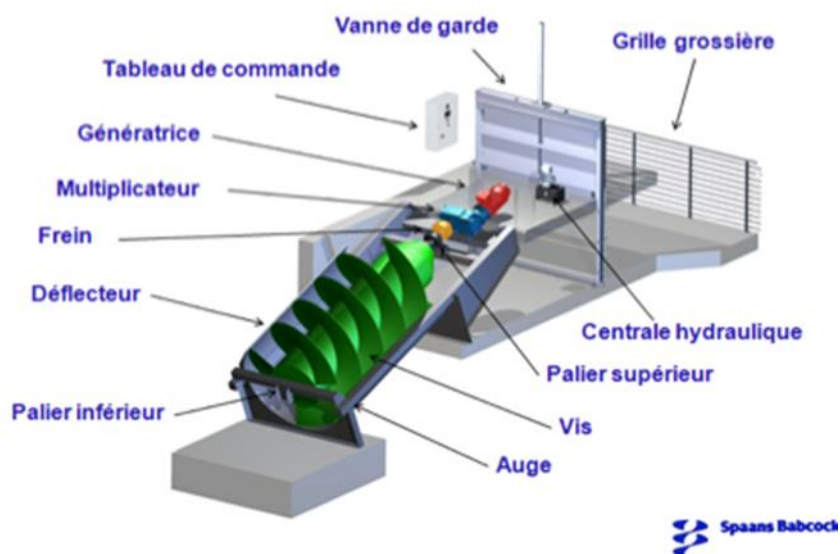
Plan 3D pour une centrale à vis d'Archimède type.
